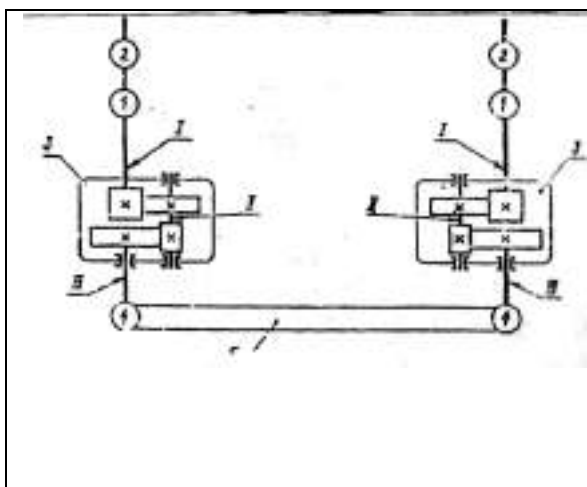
Кинематическая схема привода с коническим зубчатым редуктором:
